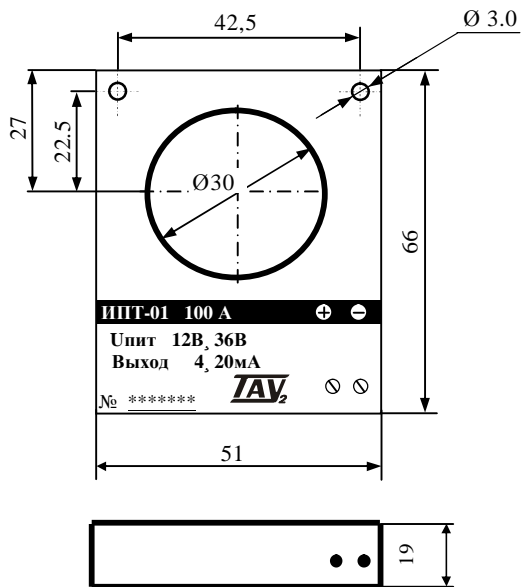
Габаритные размеры преобразователя тока измерительного ИПТ-01
